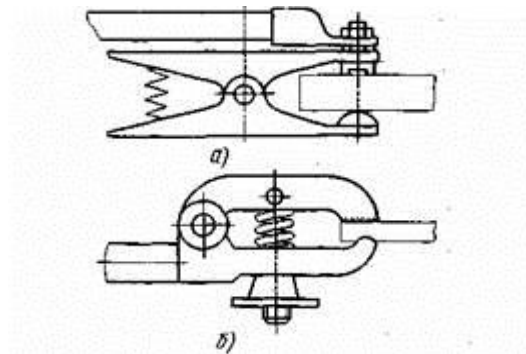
Затиски для приєднання зварювального проводу до виробу, що зварюється: а — пружинний, б — гвинтовий
